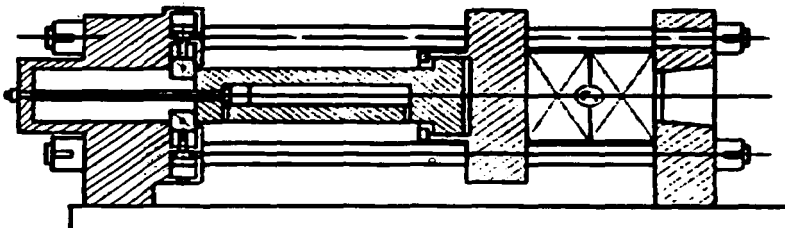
Sección longitudinal de un grupo de cierre de moldes de tipo hidromecánico o pistón bloqueado, usado normalmente en máquinas grandes.
